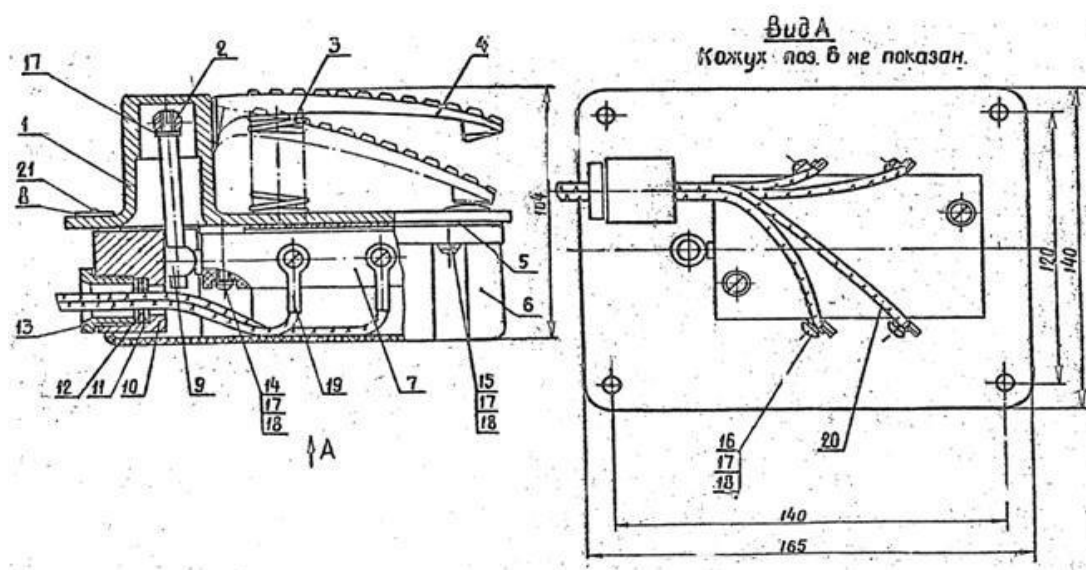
Выключатель педальный типа ВП-1-11УЗ.
